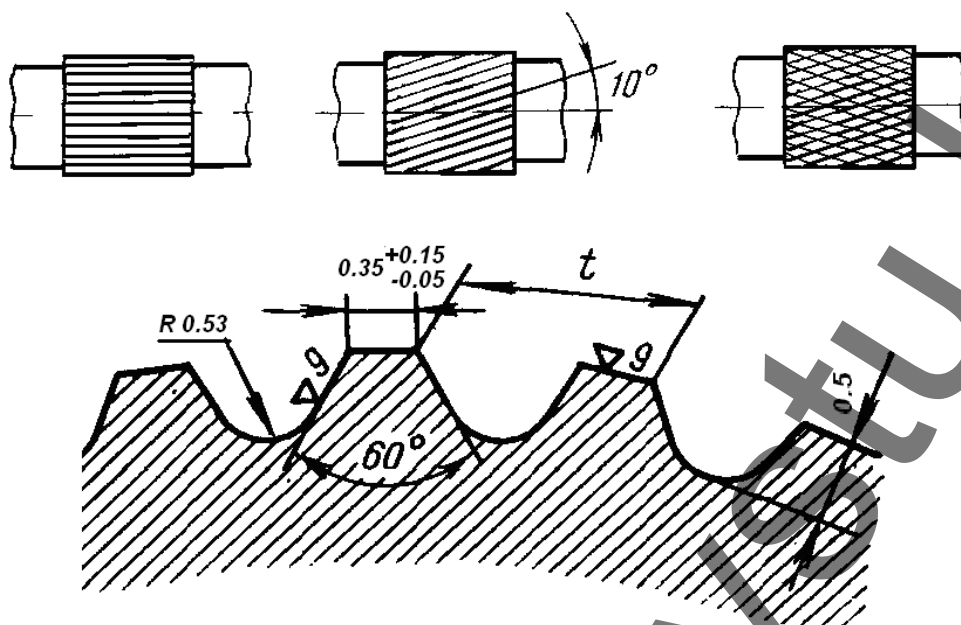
Профиль рифлей цилиндров вытяжного прибора
